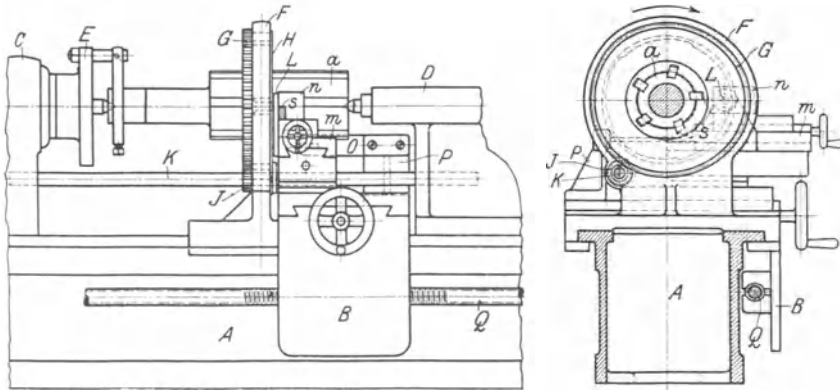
Vorrichtung zum Hinterdrehen von Gewindebohrern.
